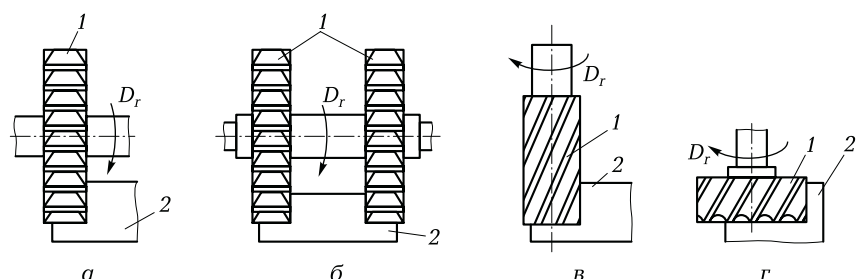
Схемы обработки уступов дисковыми (а, б), концевой (в) и торцовой (г) фрезами:
